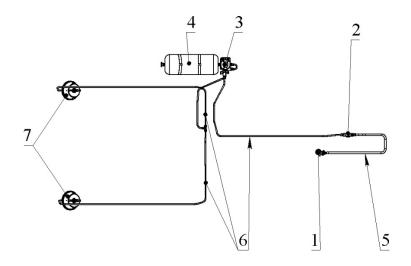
Схема пневматического привода тормозной системы кормораздатчика. 1 – головка соединительная; 2 – фильтр магистральный; 3 – воздухораспределитель; 4 – ресивер; 5 – шланг; 6 – пневмотрубопроводы; 7 – камеры тормозные.
